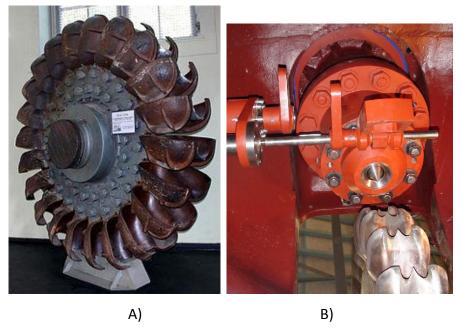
A) Rotor Pelton (Diametrul 2m; Masa 3000 kg); B) Injector
